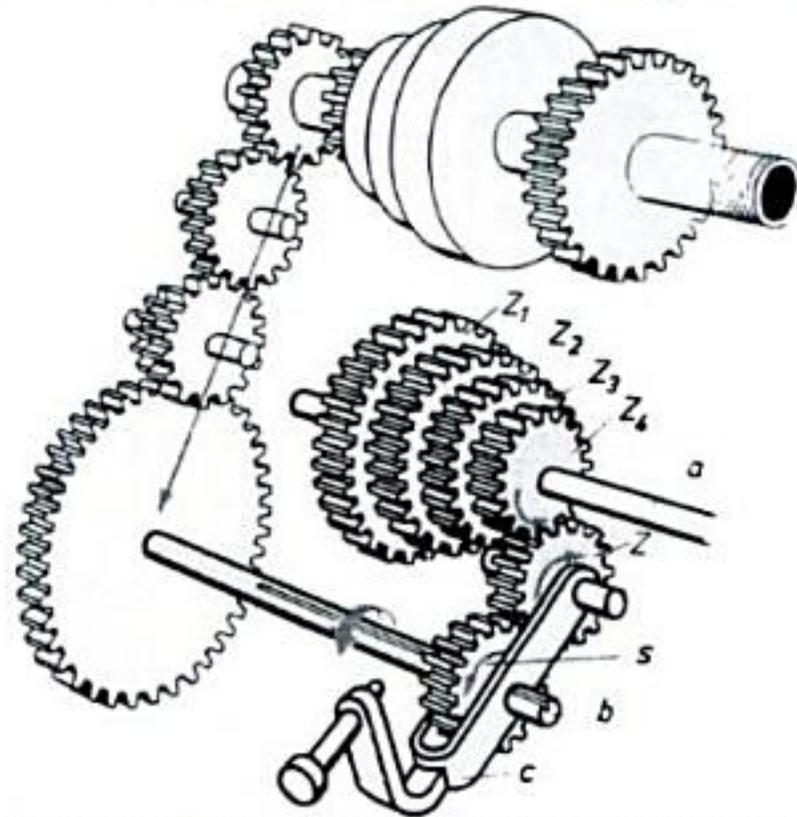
,2 Mecanismo de avance Norton: a) husillo de cilindrar; b) árbol de engranaje; c) palanca oscilante; s) rueda móvil; Z) rueda oscilante
